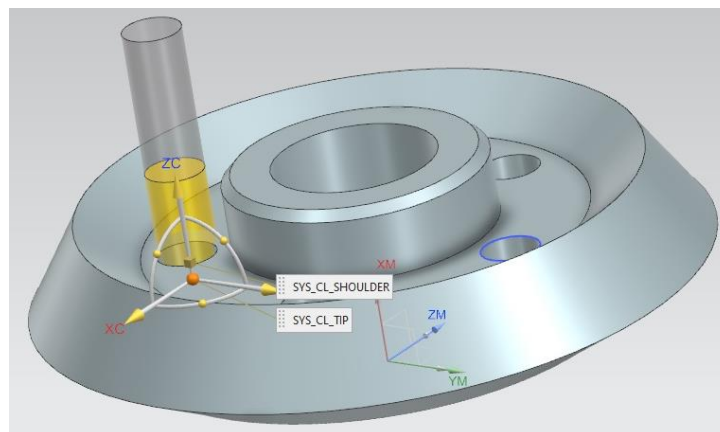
Розташування інструменту відносно поверхні обробки
